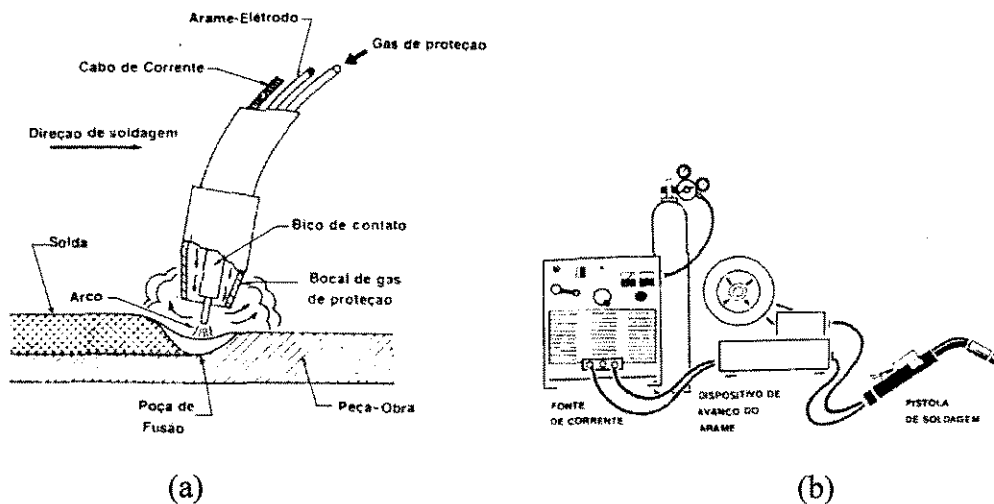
a - Representação esquemática do extremo de uma pistola de soldagem MIG.
